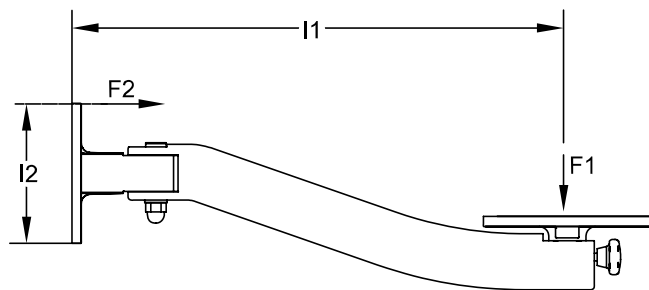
Schema di sollecitazione supporto per fissaggio a parete
